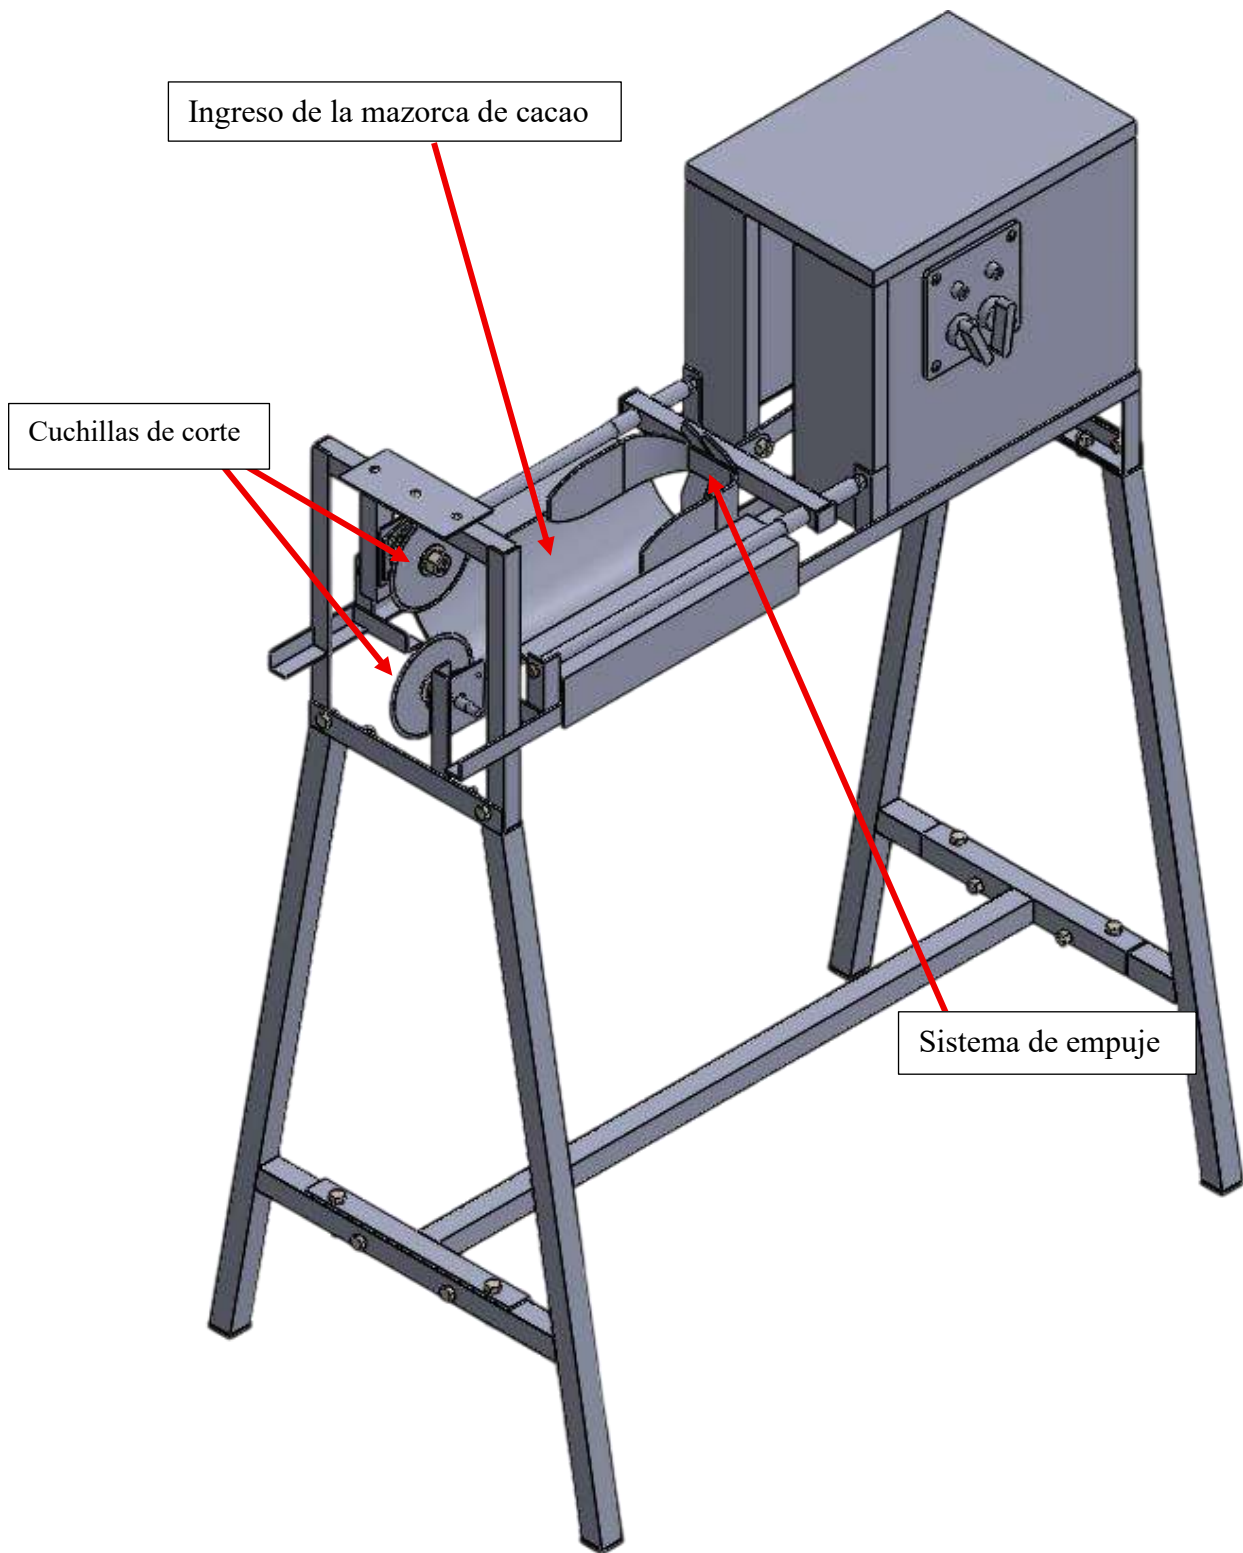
Sistema de corte de la máquina desvainadora de cacao
